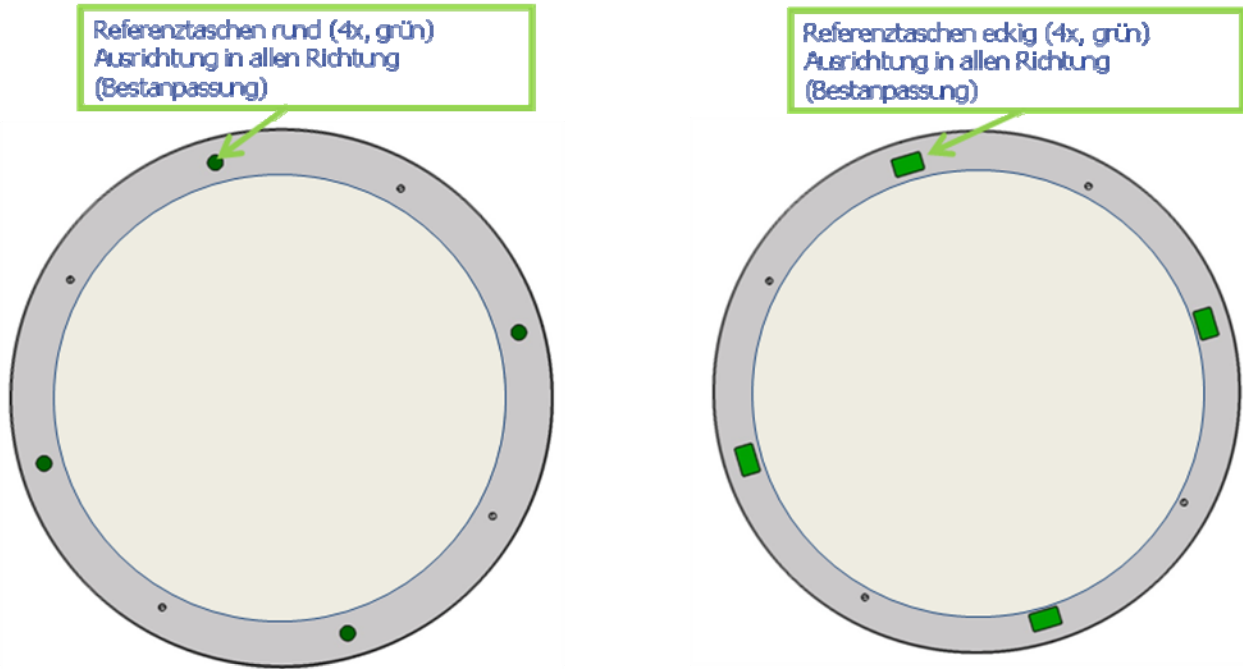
Ausrichtung für Werkzeuge, Formen und Vorrichtungen
